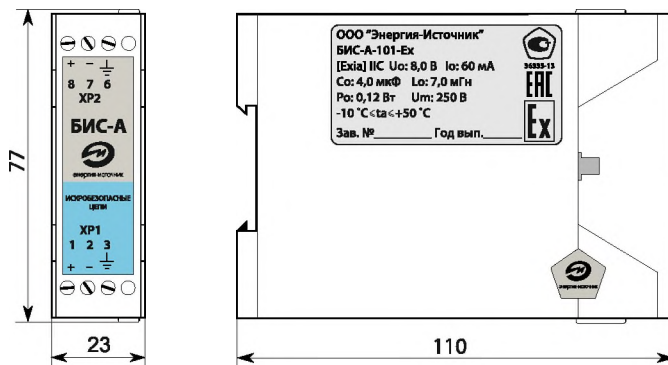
Габаритные и присоединительные размеры барьеров
